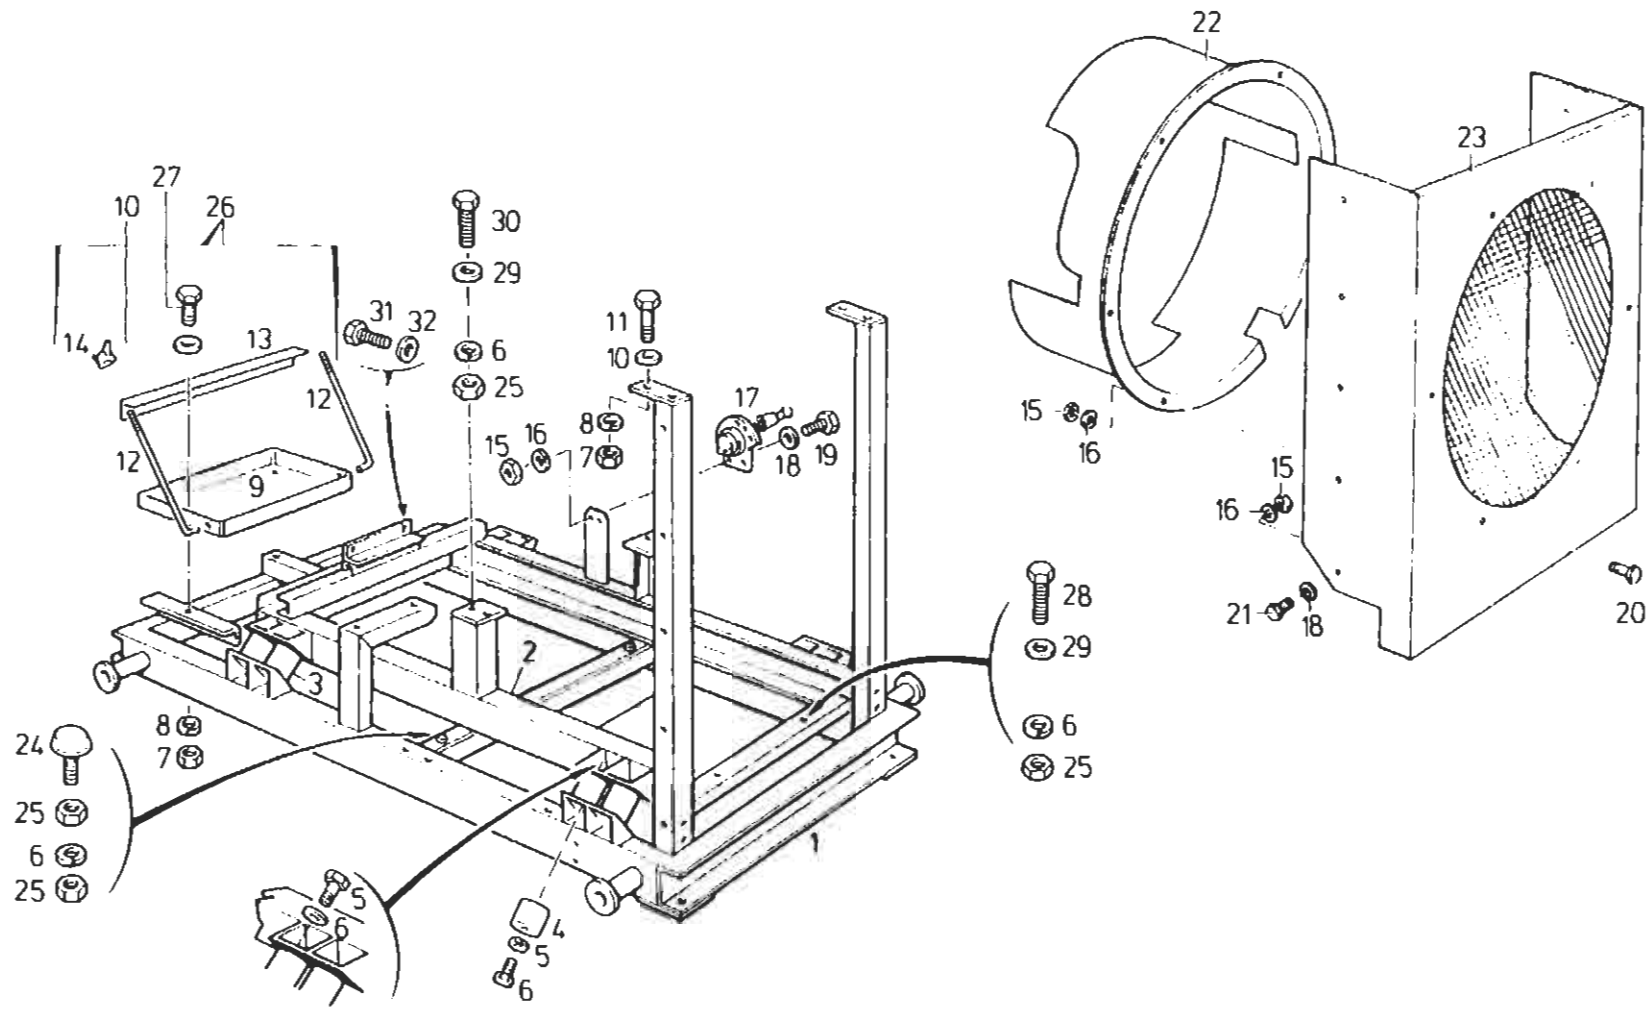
/15 Grundrahmen E u. B Ausführung
